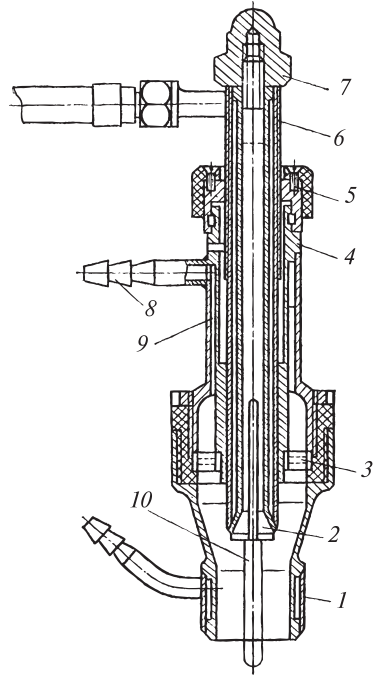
Головка для автоматической сварки неплавящимся электродом
